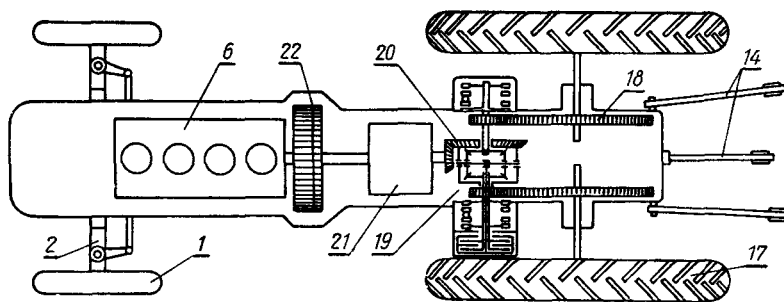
Схема расположения основных механизмов колесного трактора МТЗ-80 (обозначения те же, что на рисунке 8).
